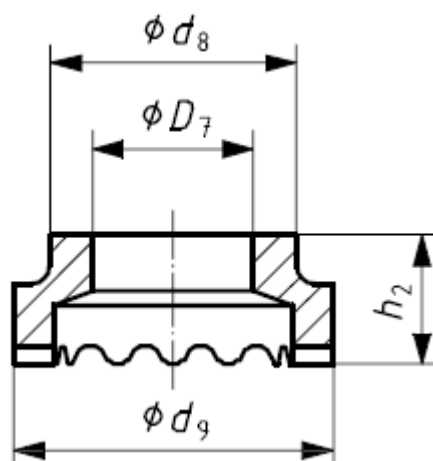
Керамическое кольцо для шпильки без резьбы и для упора (UF)
